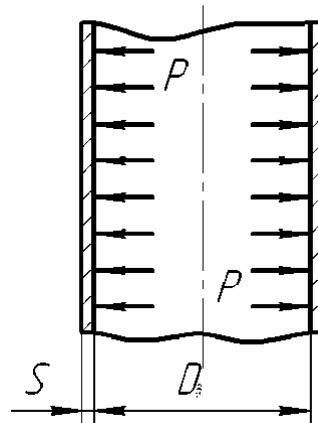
Розрахункова схема циліндричної обичайки
